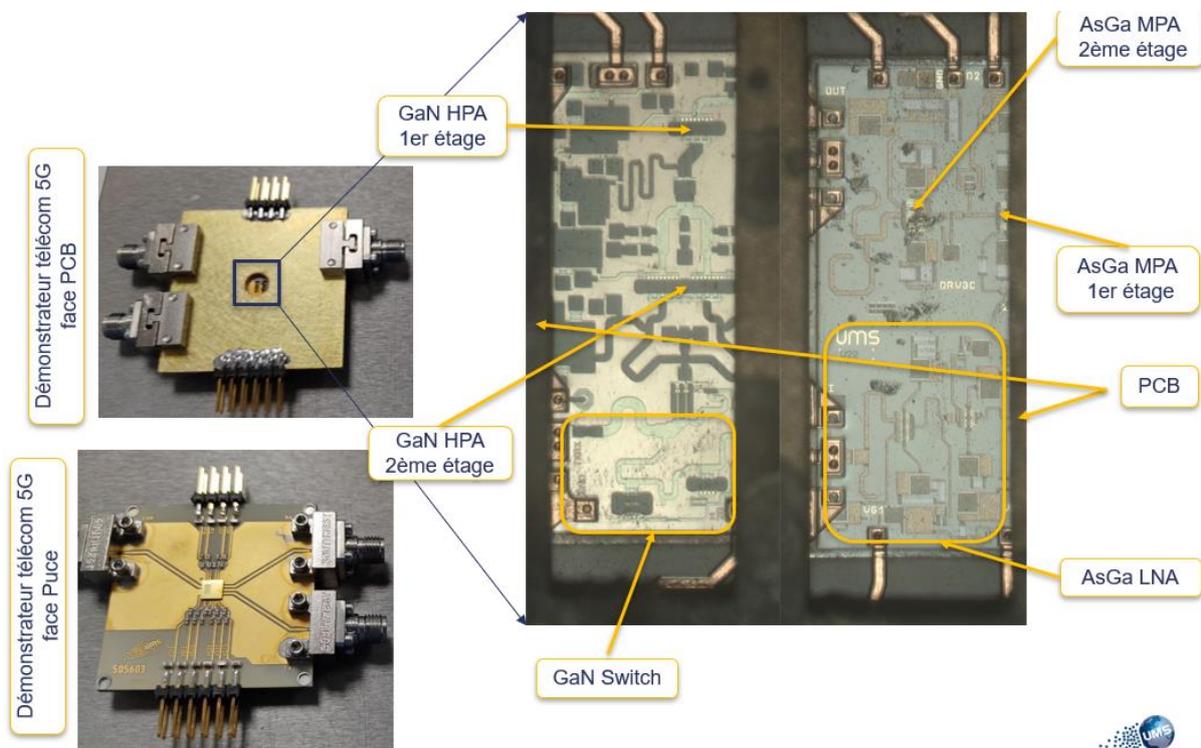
Démonstrateur télécom 5G assemblé sur PCB de la fonderie UMS
